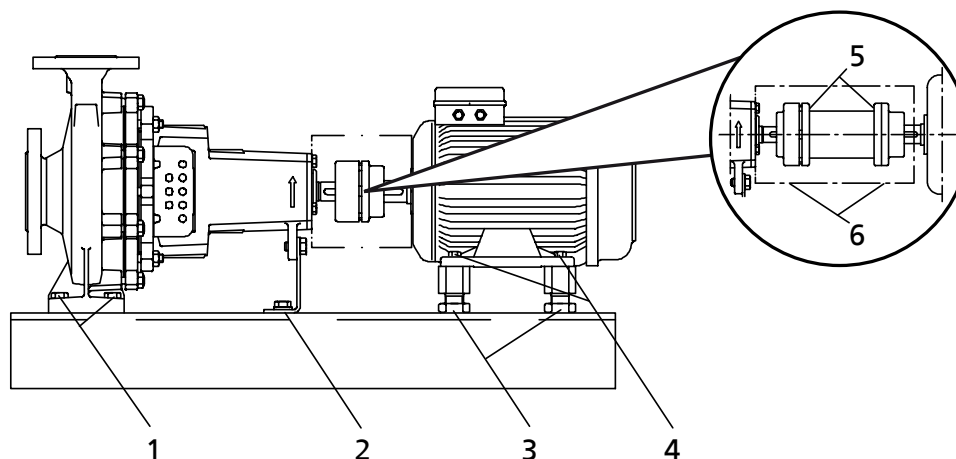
Места затяжки резьбовых соединений насосного агрегата
